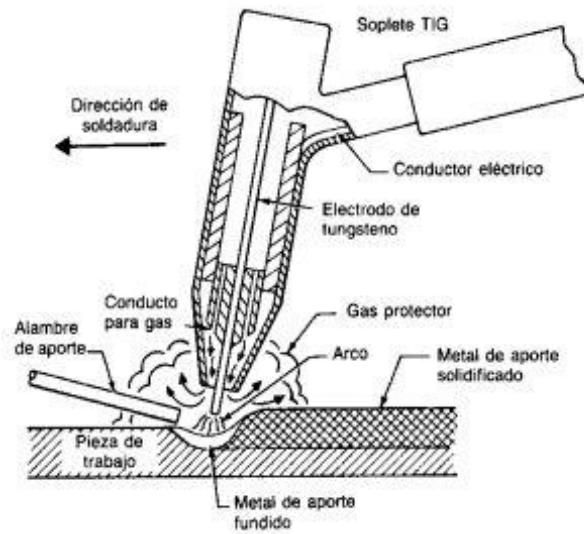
Esquema de la soldadura TIG. Fuente: <https://www.pinterest.es/pin/291397038380596173/?!p=true>
